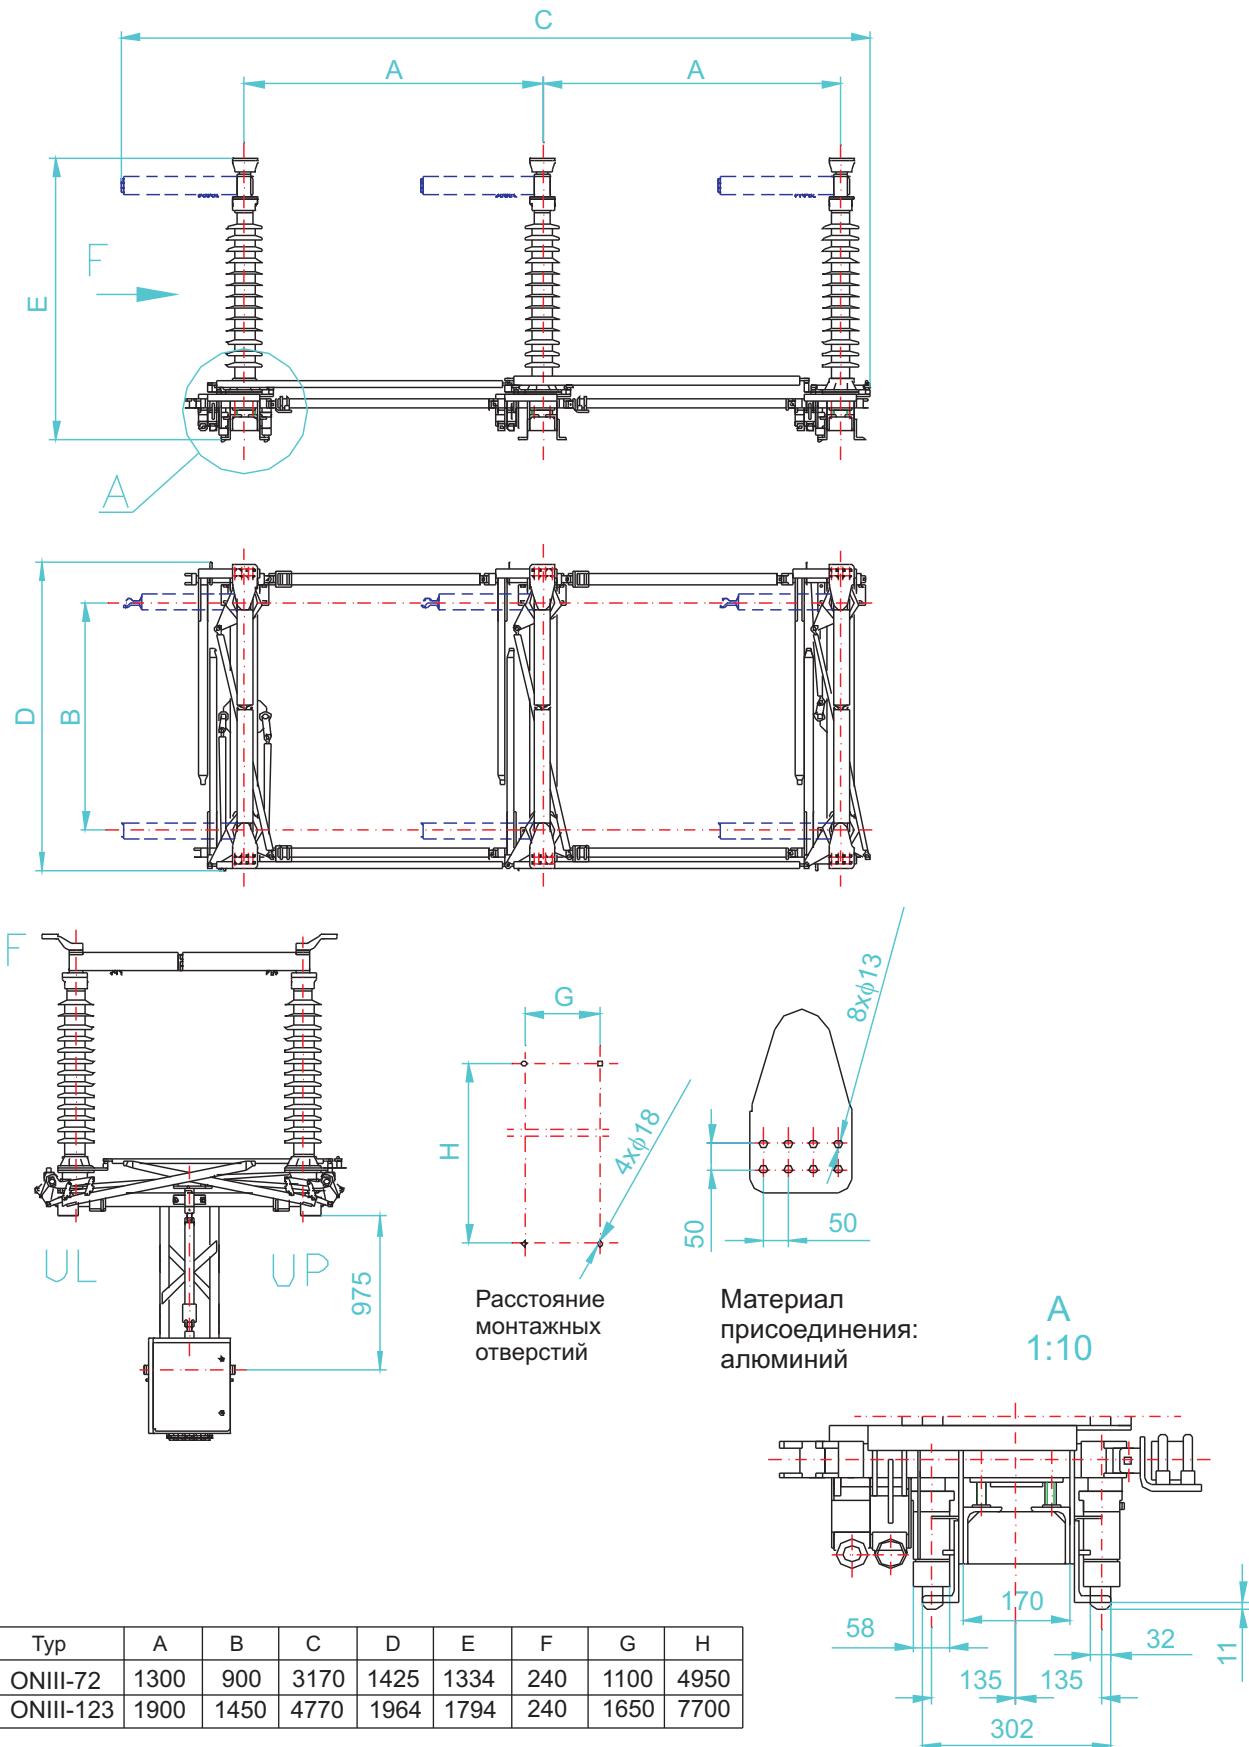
Размерный эскиз ONIII-123 и ONIII-72
